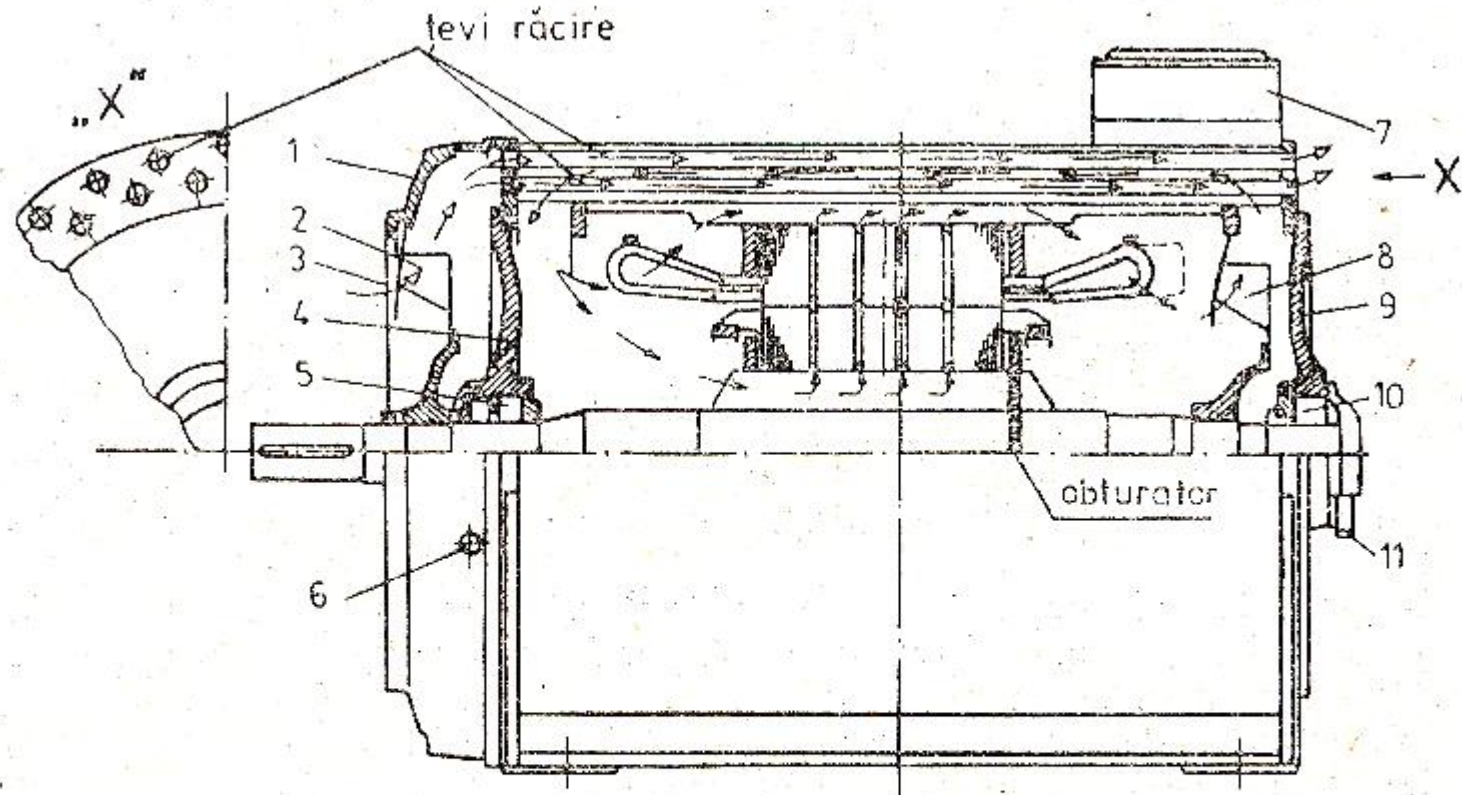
Mașină închisă cu schimbător de căldură aer-aer, constituit din țevi dispuse pe circumferința carcasei :
